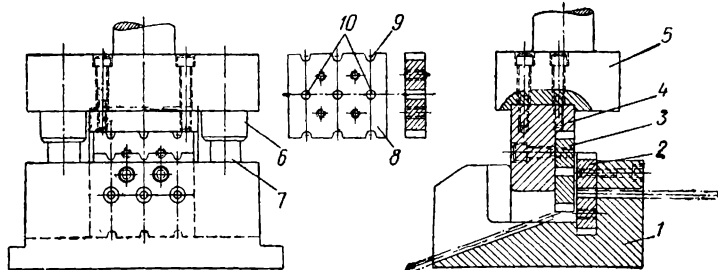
Глазковый штамп для резки калиброванной стали: 1 — плита; 2 — нижний нож; 3 — верхний нож; 4 и 5 — державки; 6 — втулка; 7 — направляющая колонка; 8 — комбинированный нож с девятью ручьями; 9 — открытый ручей; 10 — центральные ручьи-глазки
